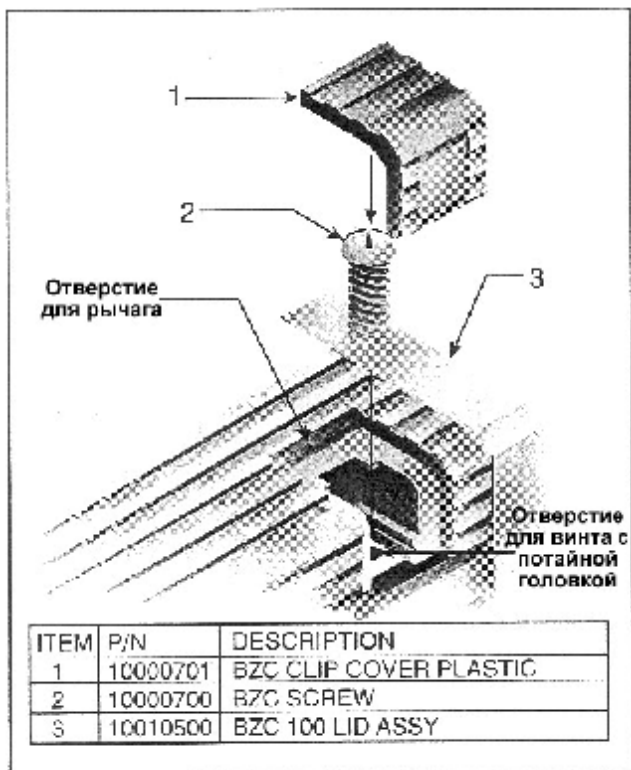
Деталь крышки контроллера Roberts Gordon® BZC 100
